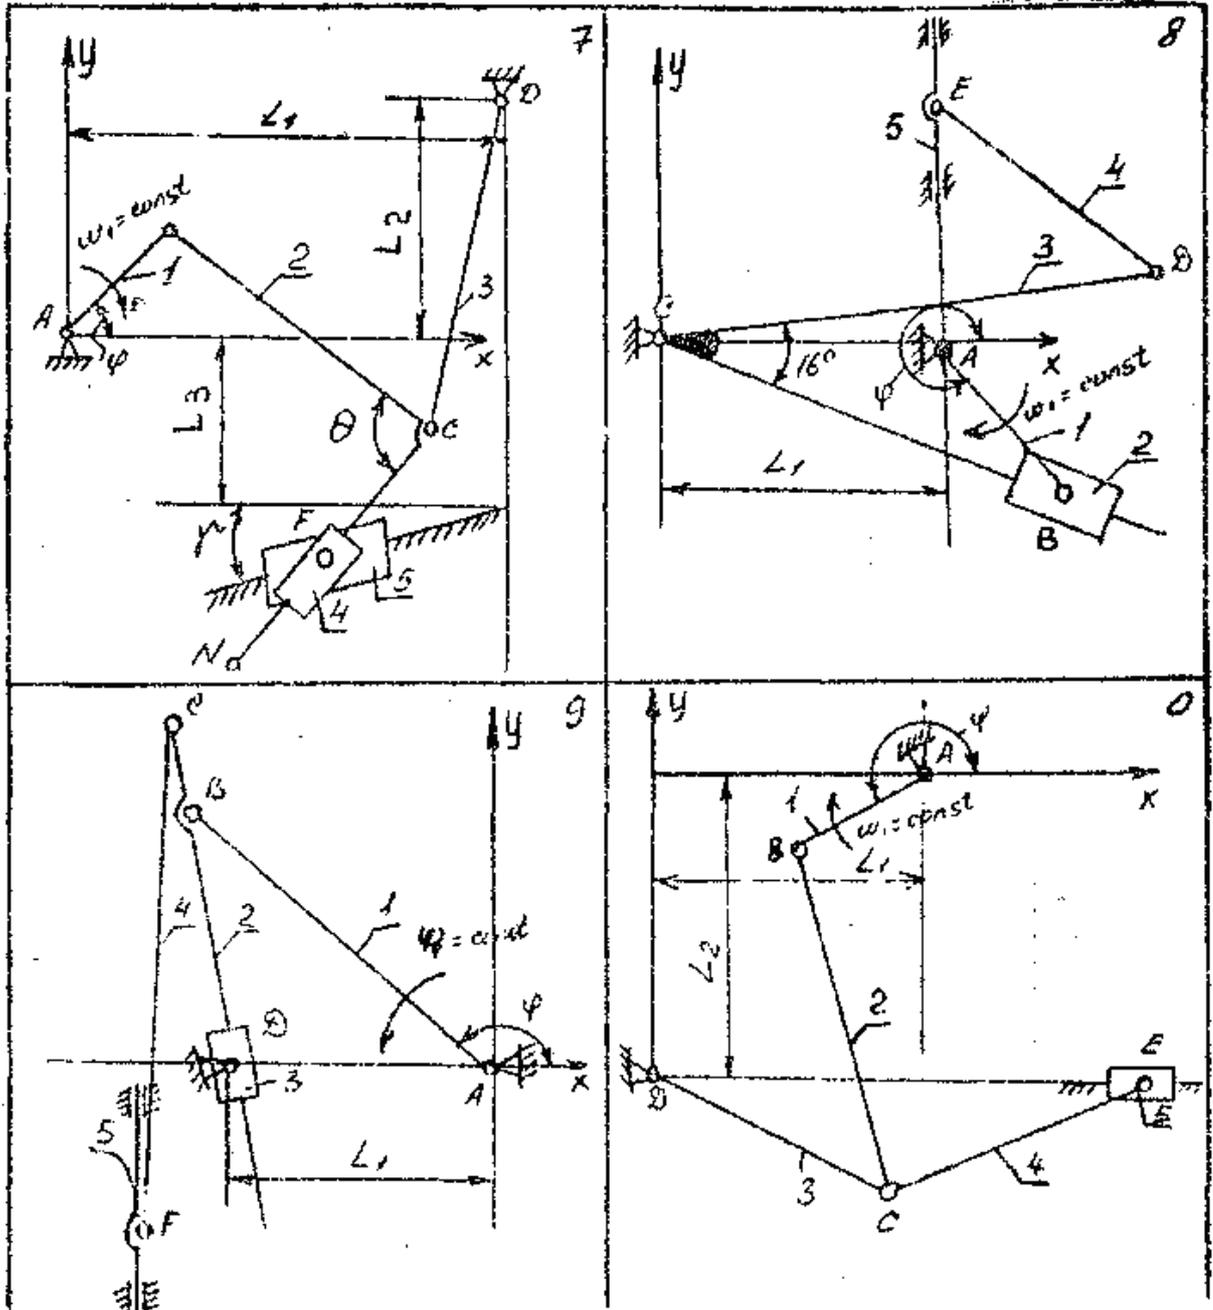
Кинематическая схема шарнирно-рычажного механизма рабочей машины (окончание)
